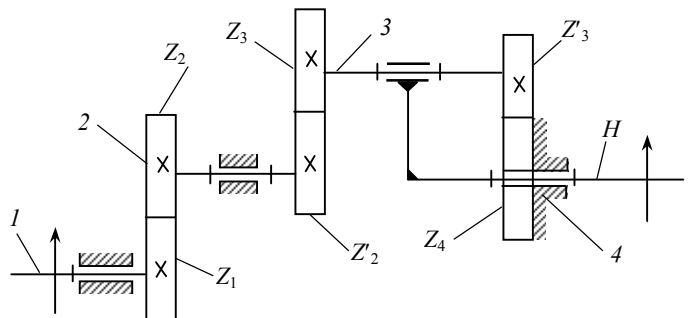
Схема редуктора аэродромного кислородного компрессора
